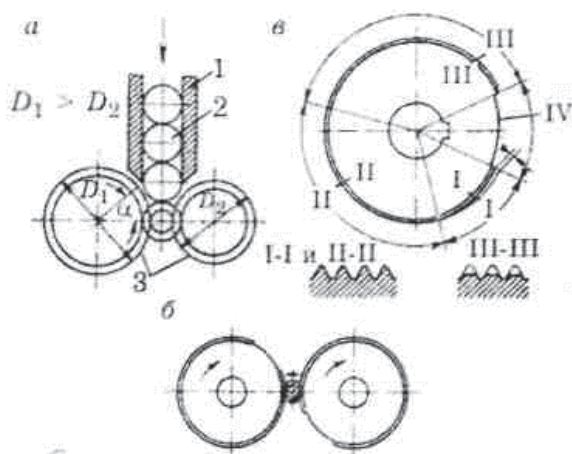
Накатывание резьбы роликами с тангенциальной подачей заготовок:
